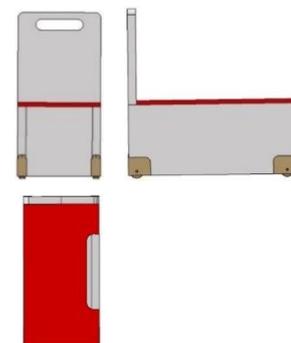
ALZADO, PLANTA Y PERFIL DEL CAJÓN PORTA JUGUETES
